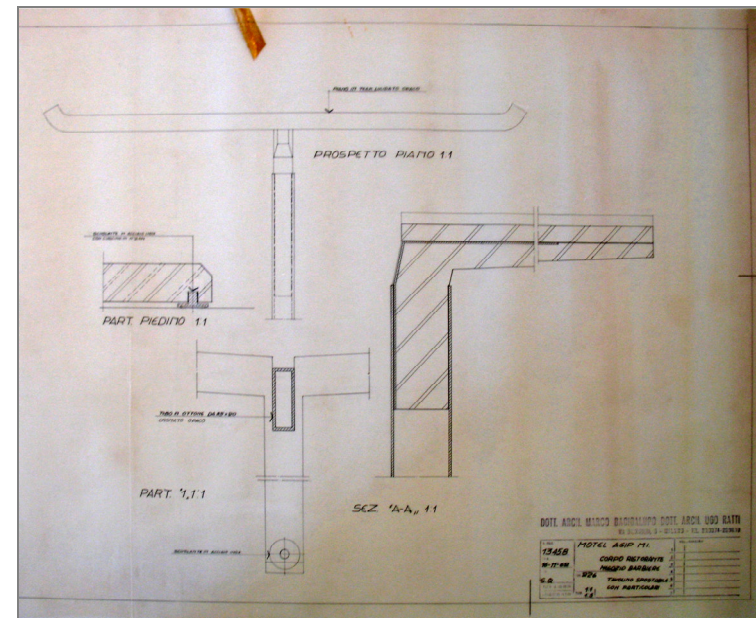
tavolino spostabile negozio parrucchiere (fonte CSAC – stralcio tav. 226, archivio n. 181-1)
